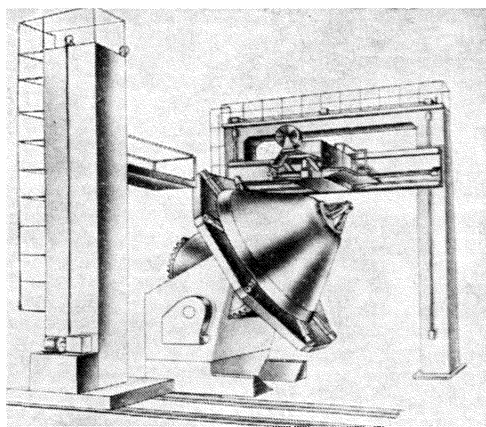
Установка У-125М для механизированной наплавки конусов
